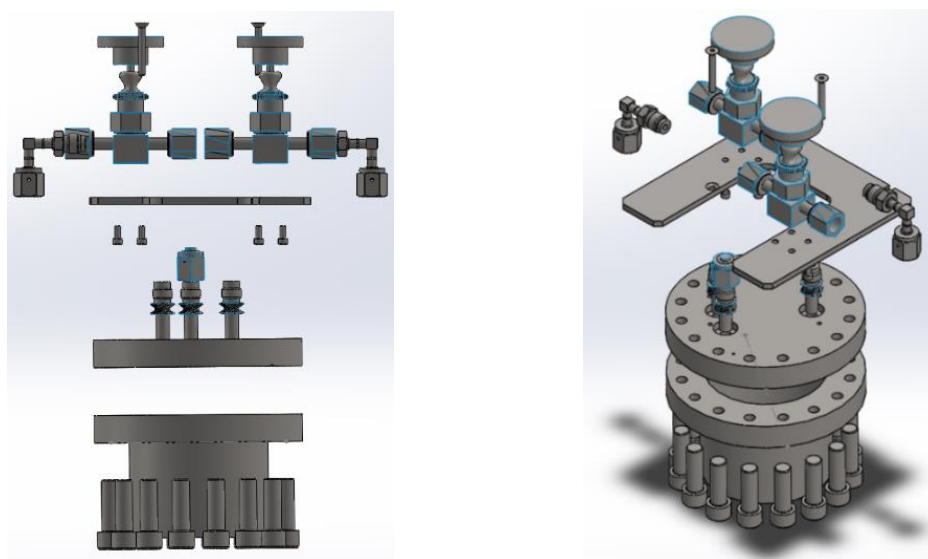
Ensamblaje del contenedor fabricado diseñado por SolidWorks.
